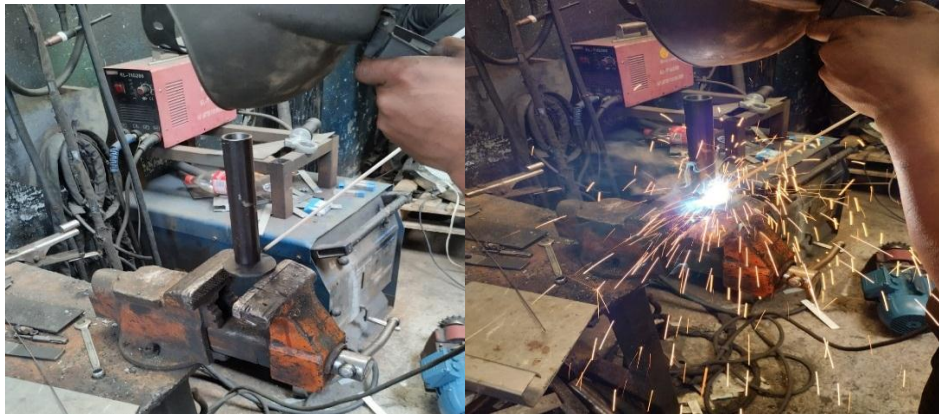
Soldadura de los soportes superiores con el bebedero.
